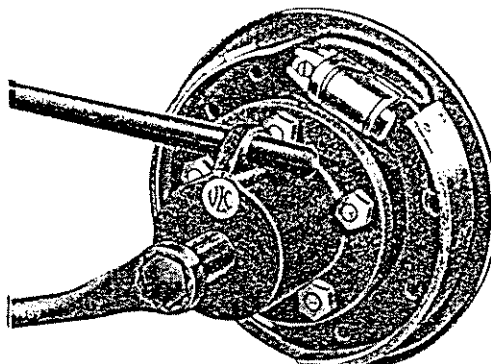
Ausbau der Hinternabe mit Werkzeug
